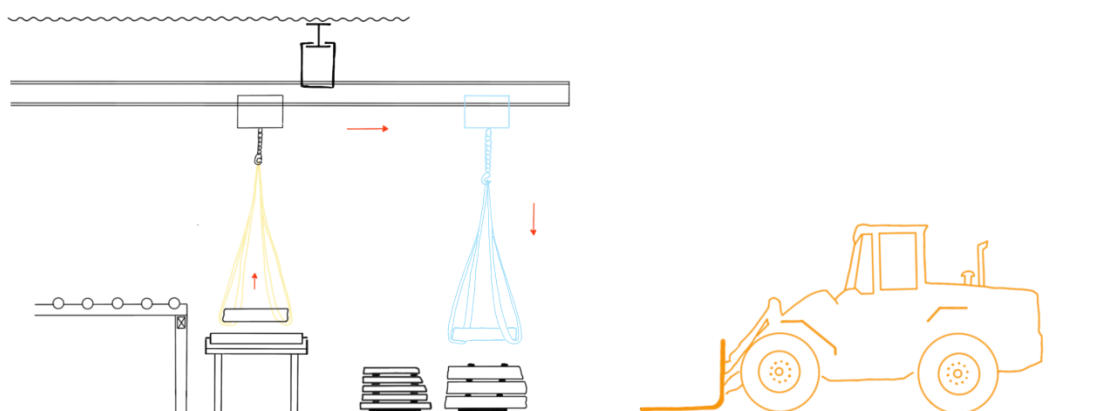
Empilhamento das chapas após passarem na granalhadora
